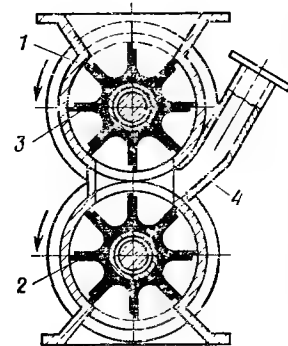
Герметичный двухлопастный шлюзовый затвор: 1, 2 — корпус; 3 — ротор; 4 — патрубок отсоса
